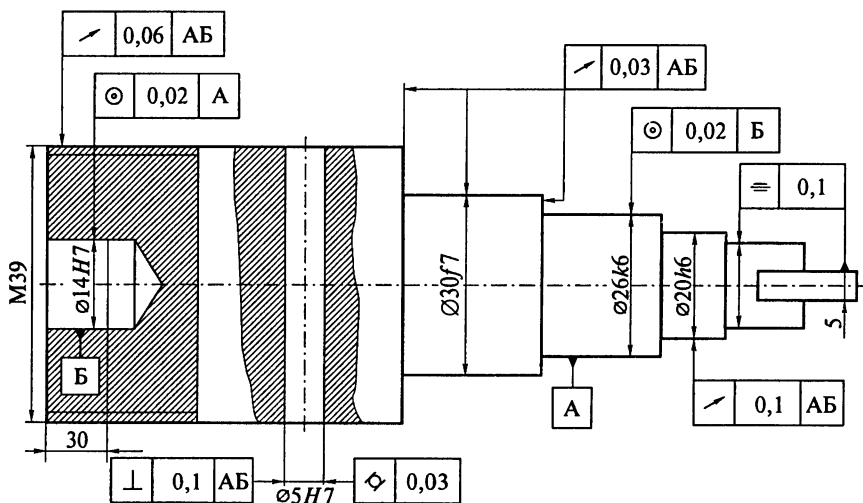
Допуски формы и расположения поверхностей на детали типа «вал»
